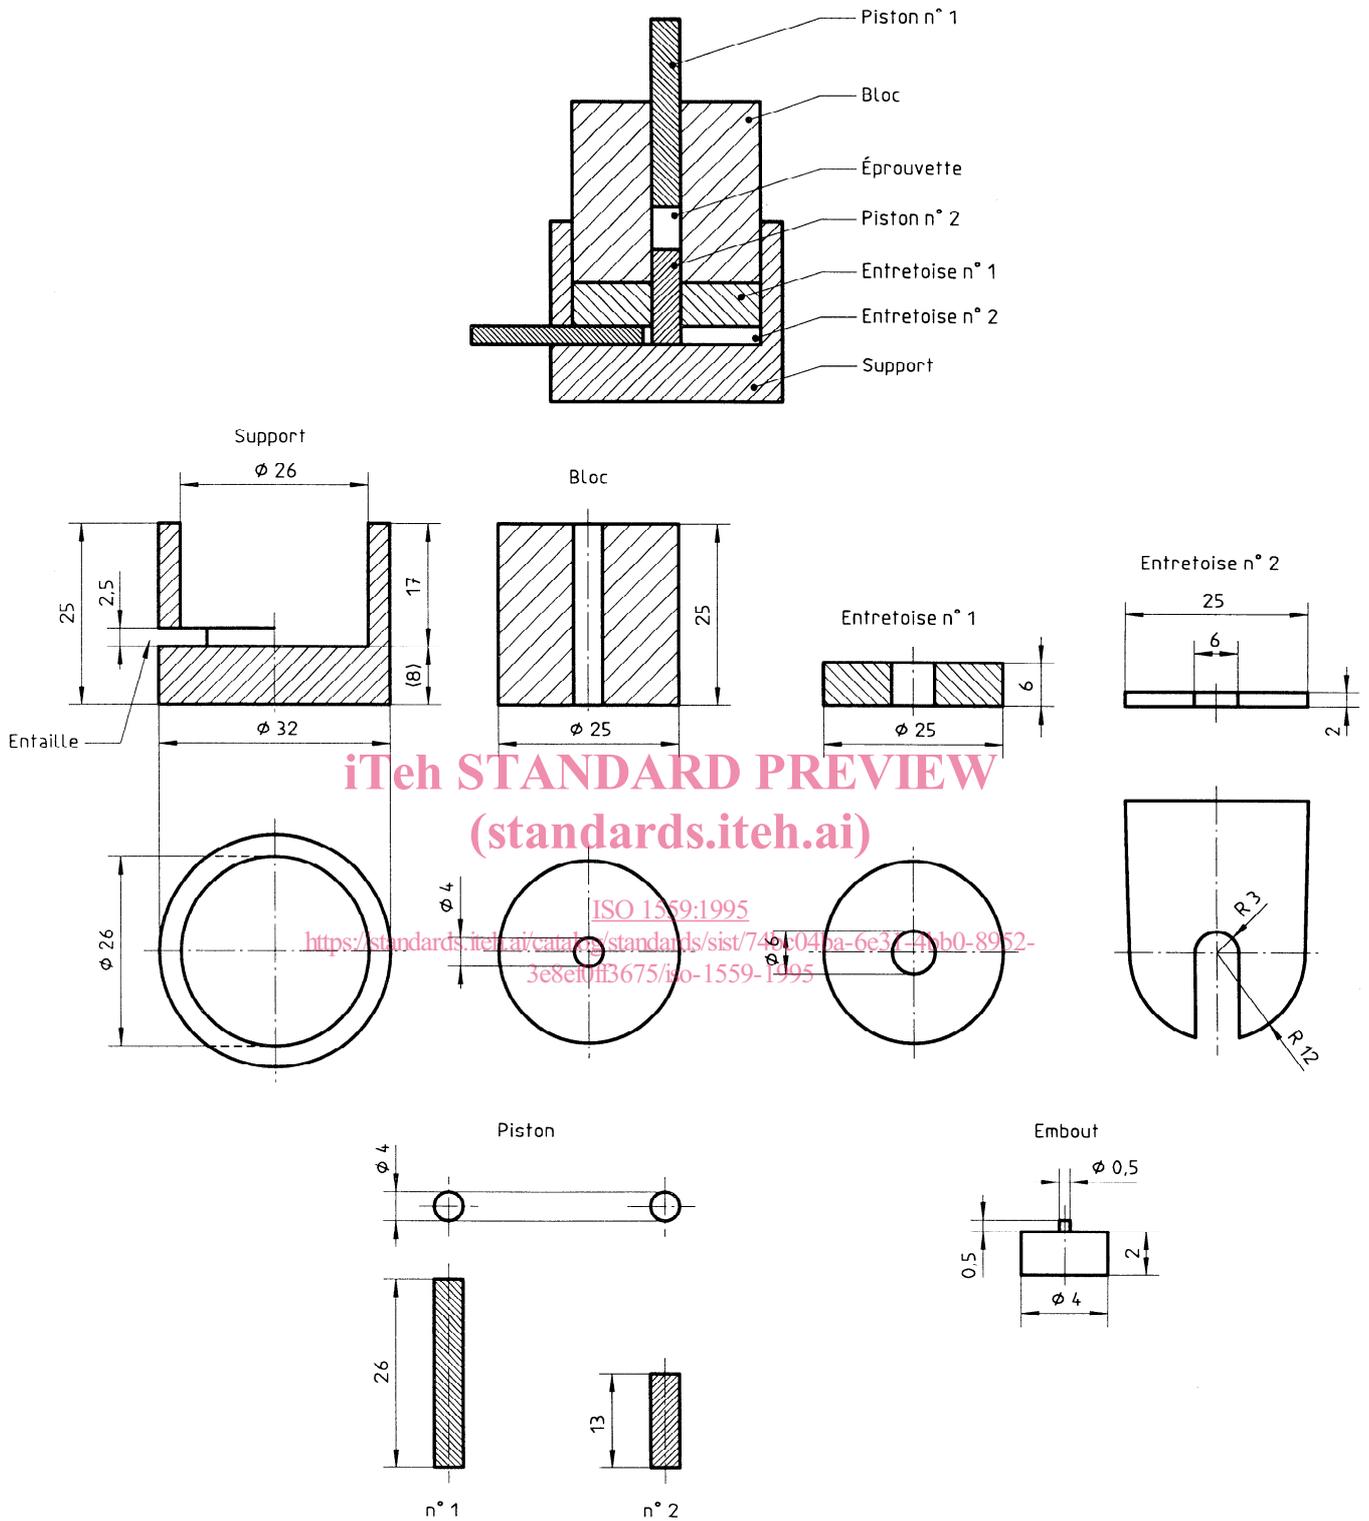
Appareillage destiné à réaliser les éprouvettes d'amalgame dentaire, montrant l'appareil assemblé et les dimensions de chaque élément
